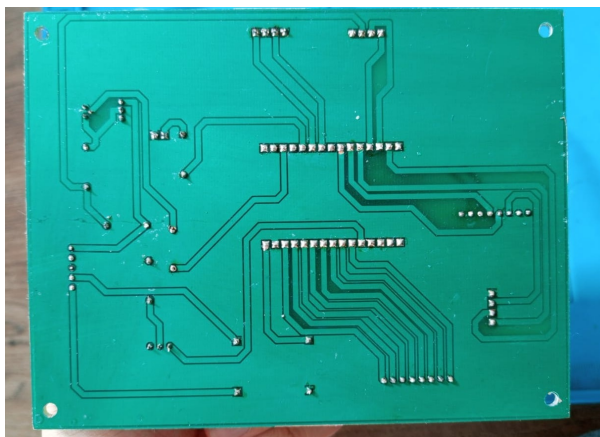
Imagen de la PCB con la soldadura ya realizada.
